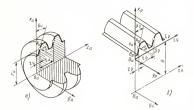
Параметры производящей поверхности дискового инструмента и инструментальной рейки
